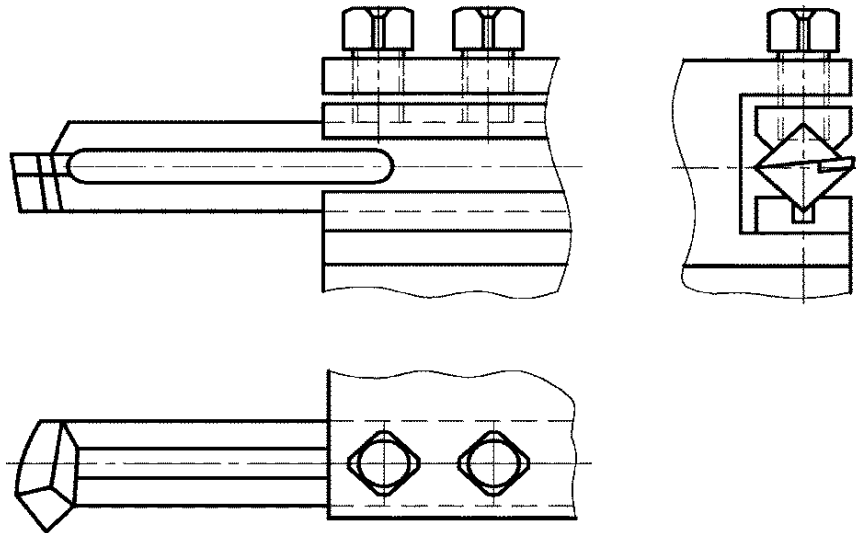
Нескрученный расточный резец конструкции В. К. Семинского, установленный с помощью приспособления в резцедержателе
